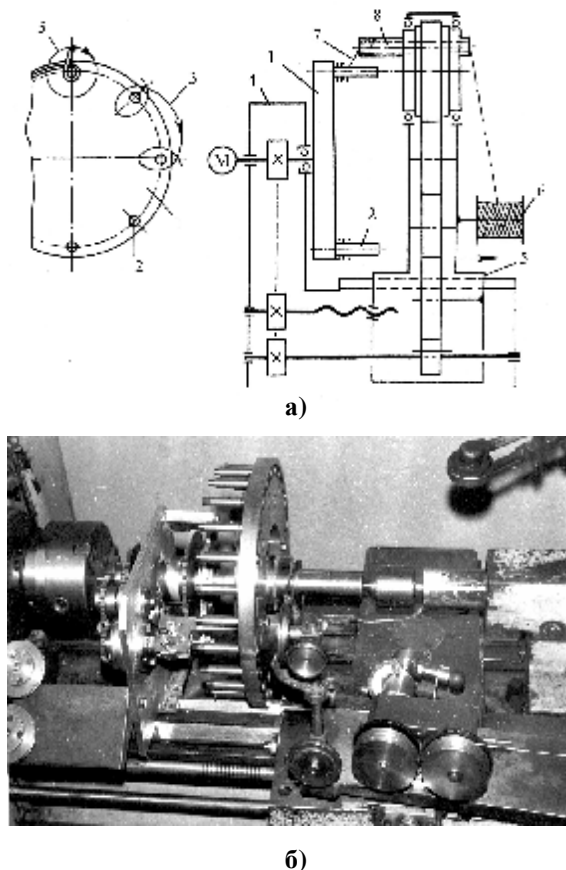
Кінематична схема (а) і зовнішній вигляд (б) складального верстата зубчастих пасів з ВПА зубів: 1 – планшайба; 2 – штифти, 3 – траєкторія руху кордоводила; 4 – станина; 5 – супорт; 6 – навій з кордом; 7 – кордшнур; 8 – кордоводило
